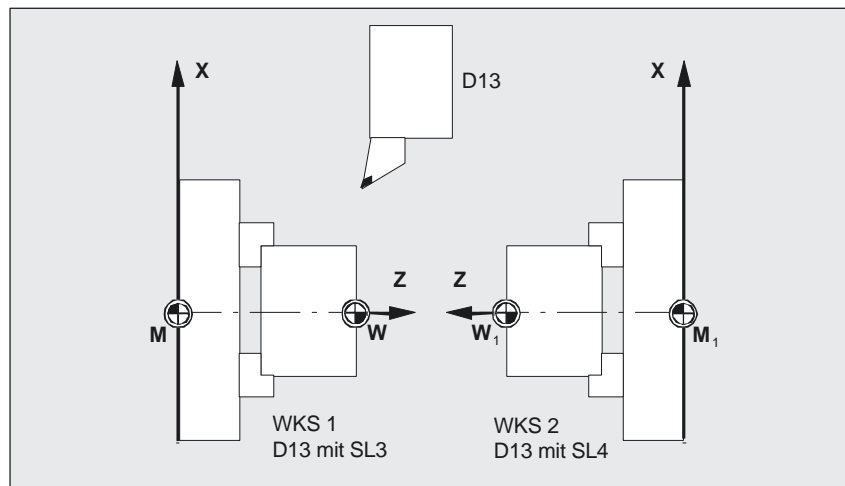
Beispiel für Werkzeuglängen spiegeln
